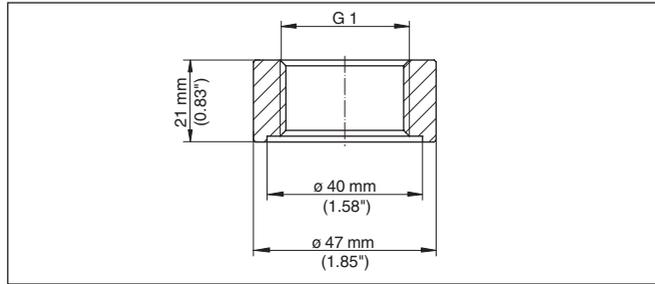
Dimensions raccord à souder G1 (DIN 3852-X)
